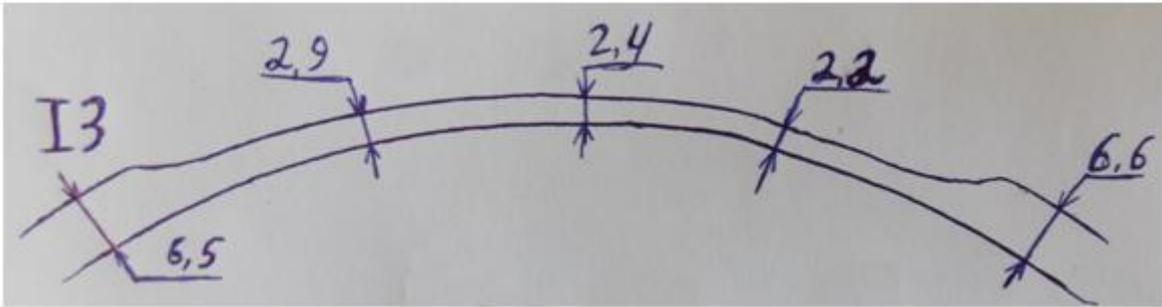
Обведенный контур сечения дефекта в кольцевом направлении после разрушения образца I3.
